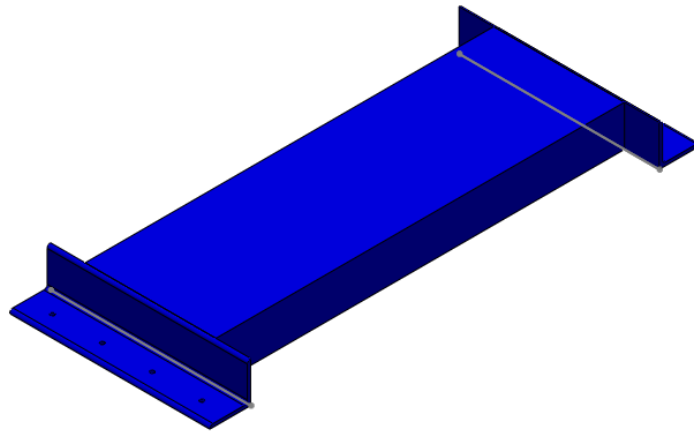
Base de la Máquina Charpy. (Fuente: El autor)
